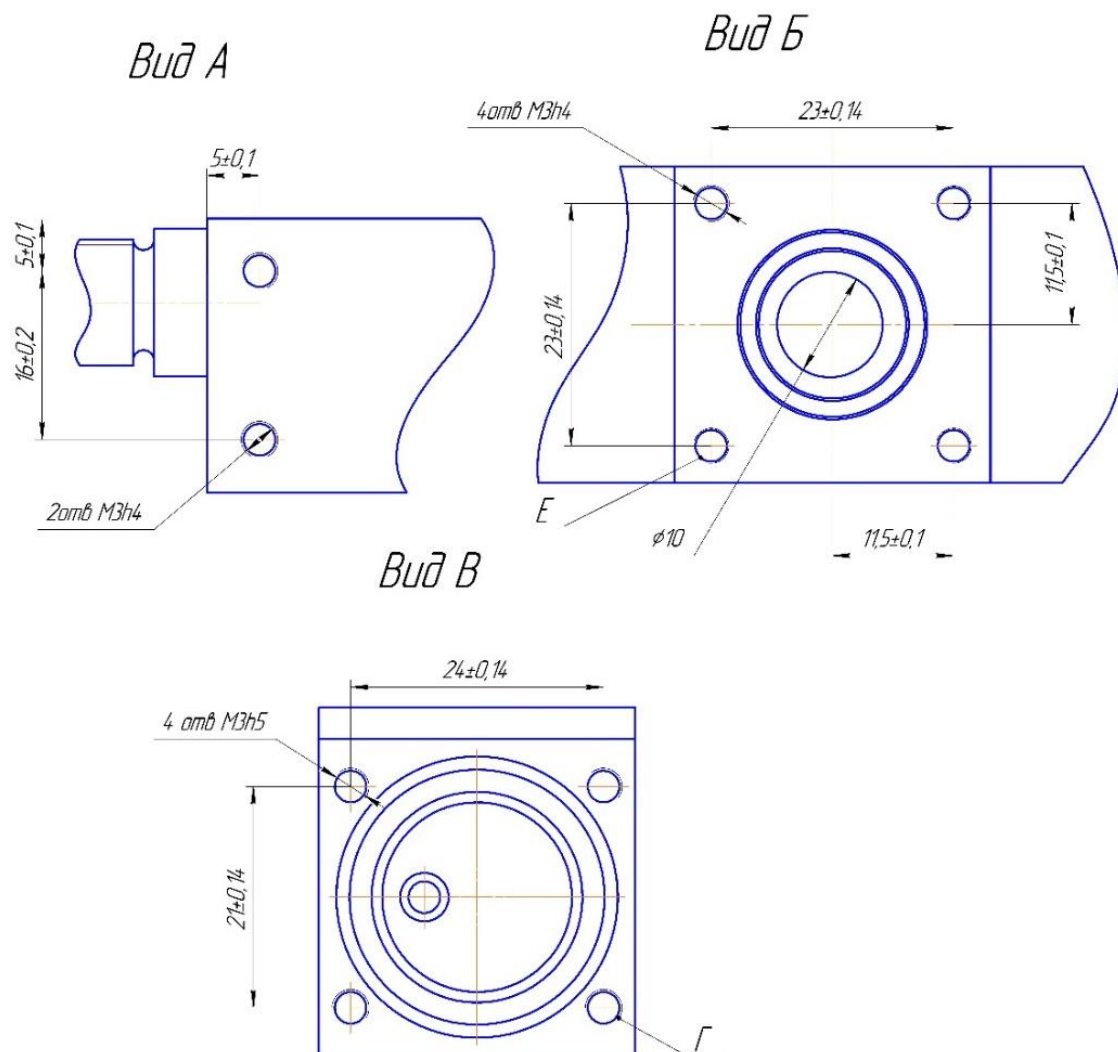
Деталь «Корпус влагопоглатителя»
